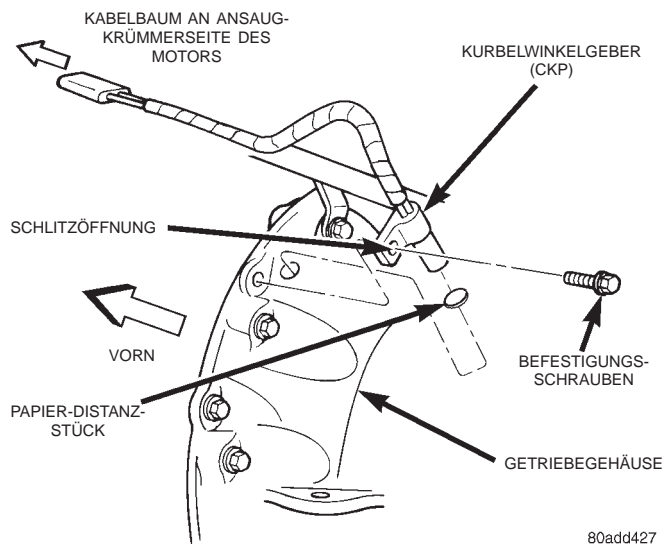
Kurbelwinkelgeber (CKP)—4.0L-Sechszylindermotor—Fahrzeuge mit Automatikgetriebe
